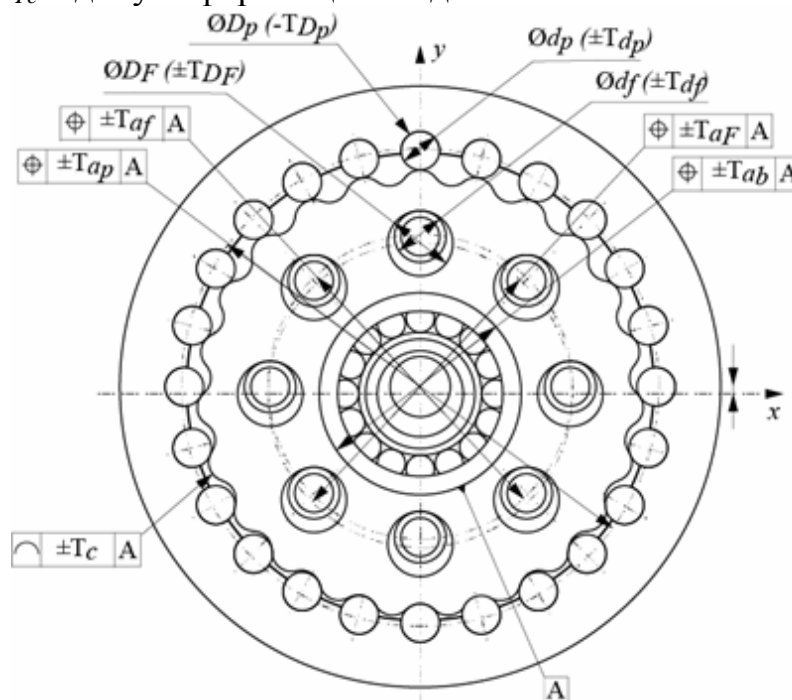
Рассматриваемые допуски планетарно-цевочной передачи
